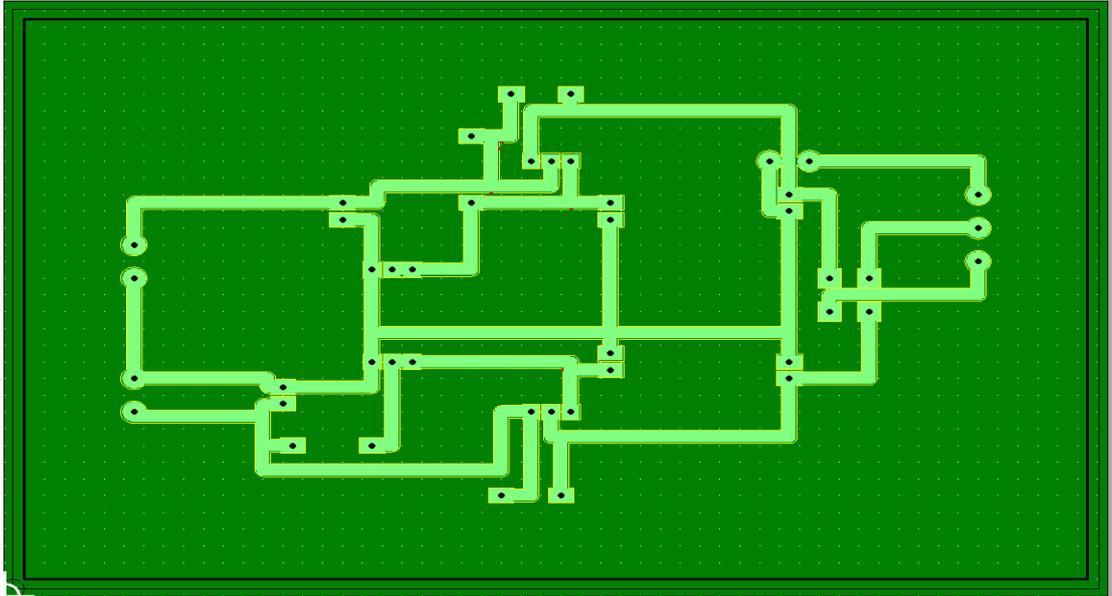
Muestra el número en que el ENGRAVING TOOL pasara diseñando cada pista.
